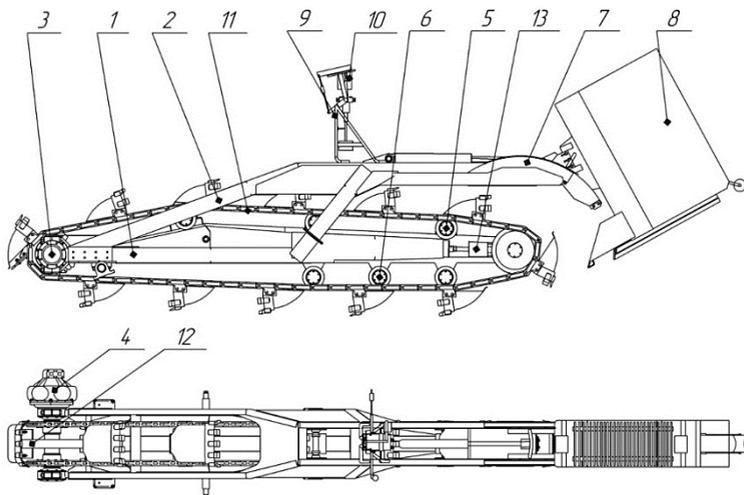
Рабочий орган: 1 – рама нижняя; 2 – рама верхняя; 3 – приводной механизм; 4 – гидромотор; 5 – поддерживающий ролик; 6 – опорный ролик; 7 – направляющий механизм; 8 – трубоукладчик; 9 – компенсирующее устройство; 10 – направляющий кронштейн; 11 – ковшовая цепь; 12 – очиститель ковшей; 13 – натяжное устройство
